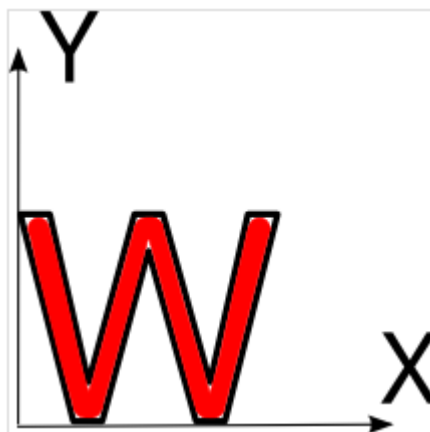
Приклад обробки літери на вертикально-фрезерному верстаті з ЧПК
